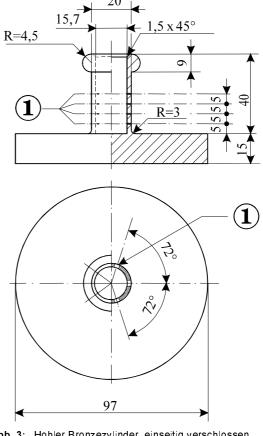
Hohler Bronzezylinder, einseitig verschlossen Aufriss und Grundriss; Maße in mm
